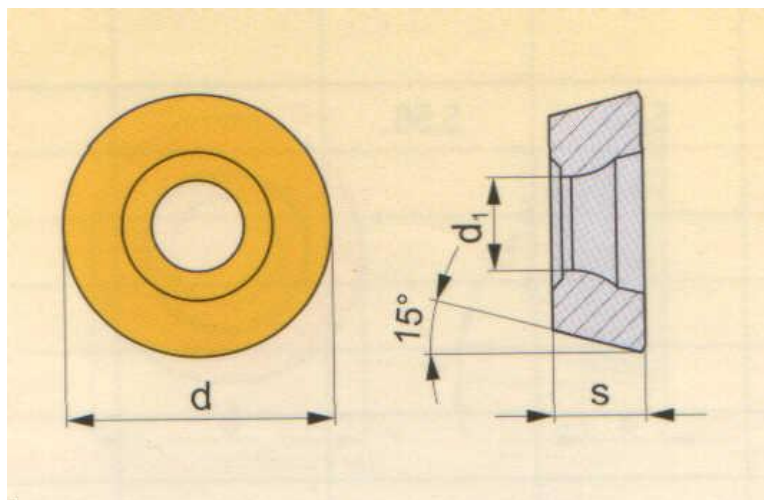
Fréza Aufsteckfräser R8-R10 RDHX
